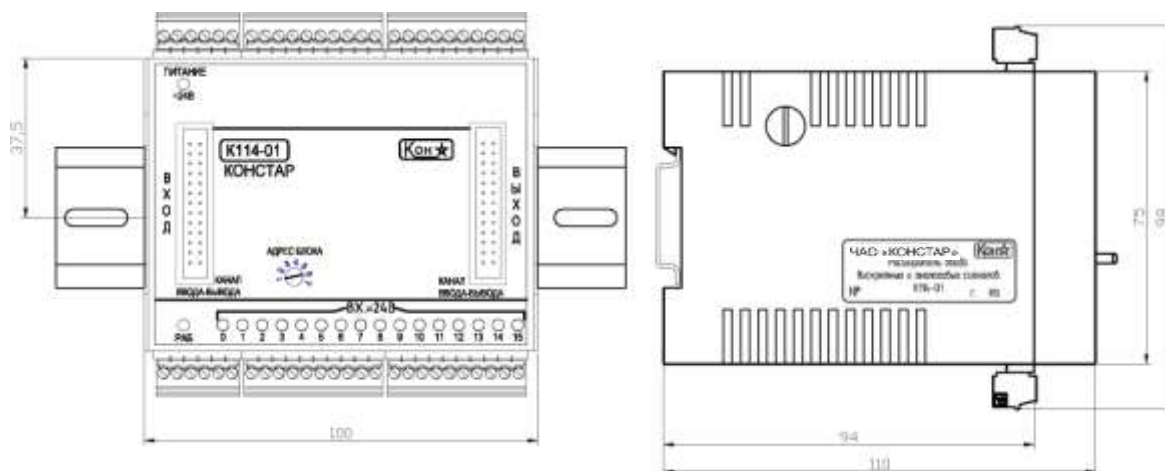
Габаритные и установочные размеры блока расширения K114 (K111)
